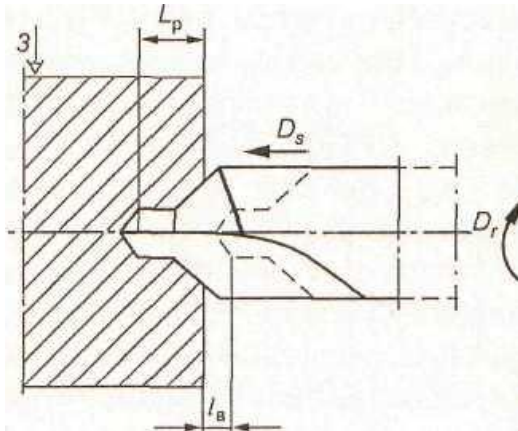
Схема центрирования отверстия вала комбинированным центровочным сверлом
